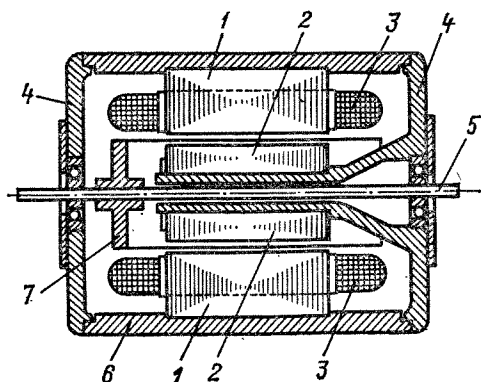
Устройство асинхронного исполнительного двигателя с полым немагнитным ротором
